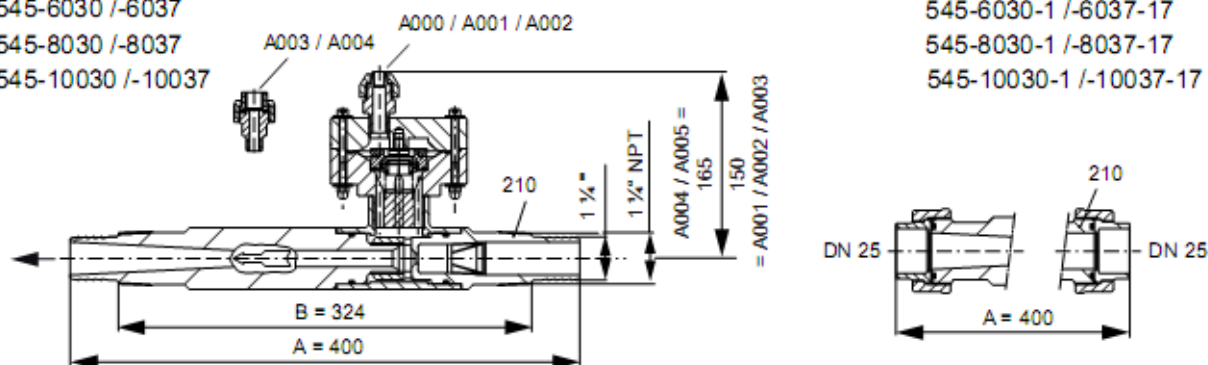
Габаритные размеры инжекторов 545-6030 до 545-10037
